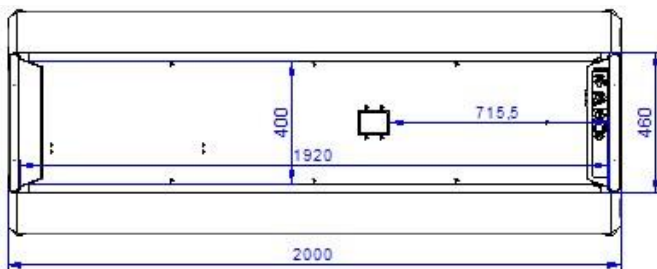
; Dimensions de la plateforme en mm, 2 pantographes
